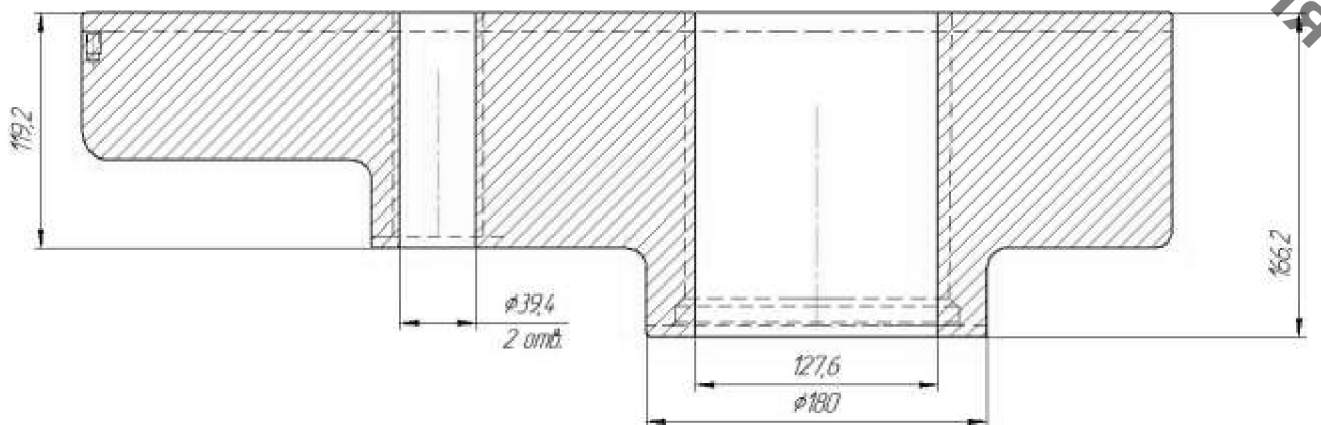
Ескіз заготовки в оболонковій форми
